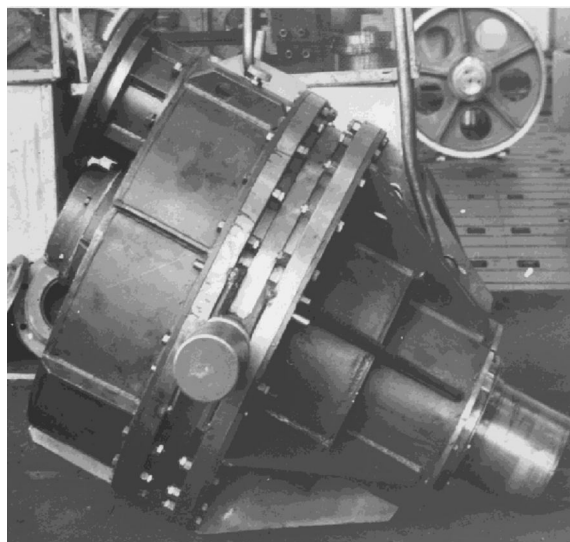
Редуктор с промежуточными телами качения привода классификатора
